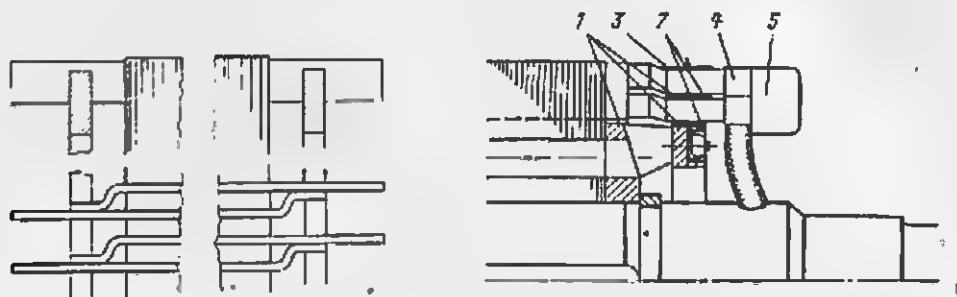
Принципиальная конструкция сварной алюминиевой кассеты ротора двигателей с $h > 355$ мм.
